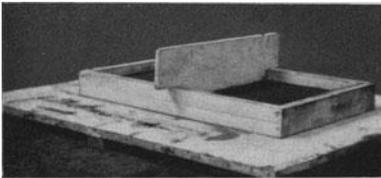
Ausziehen des Sandes auf gleichmäßige Höhe.
